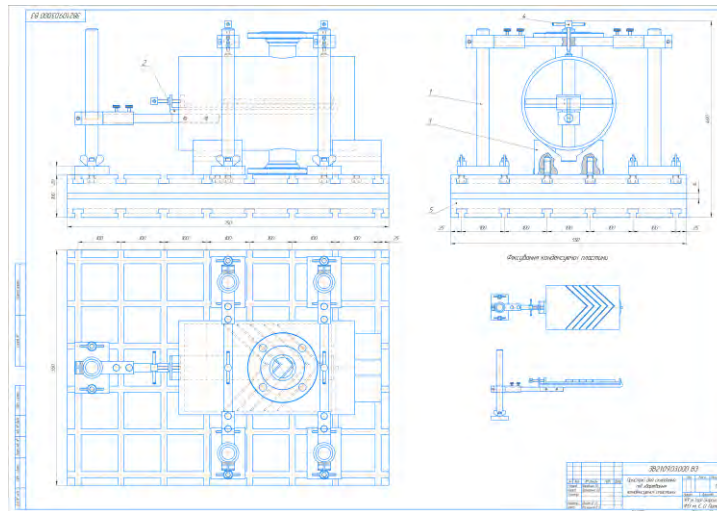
Пристрій для складання під зварювання конденсуючої пластини
